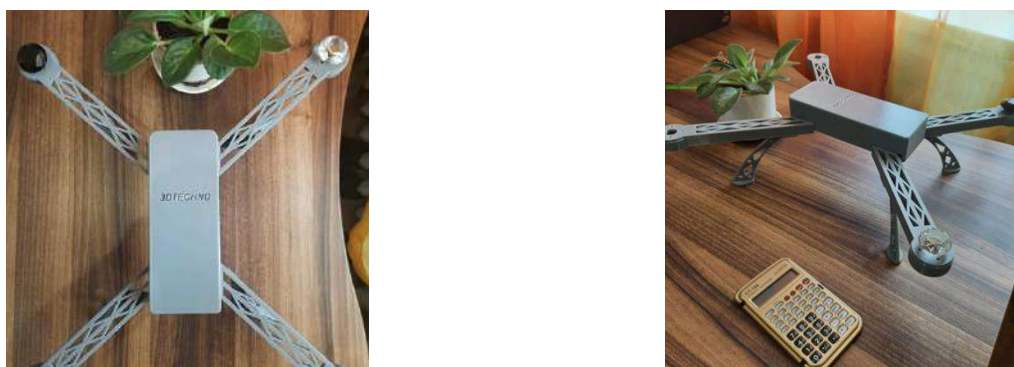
Корпус БПЛА, выполненный на 3D принтере
